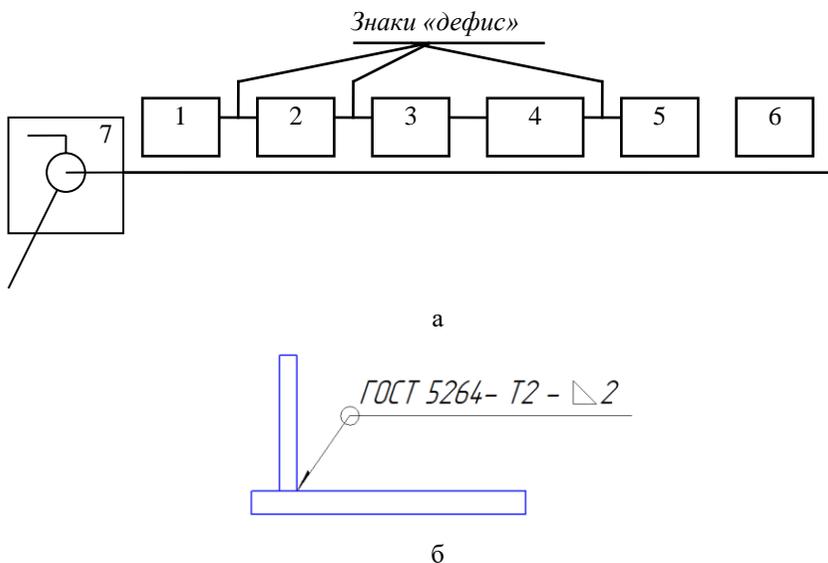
Структура и пример обозначения стандартного сварного шва
